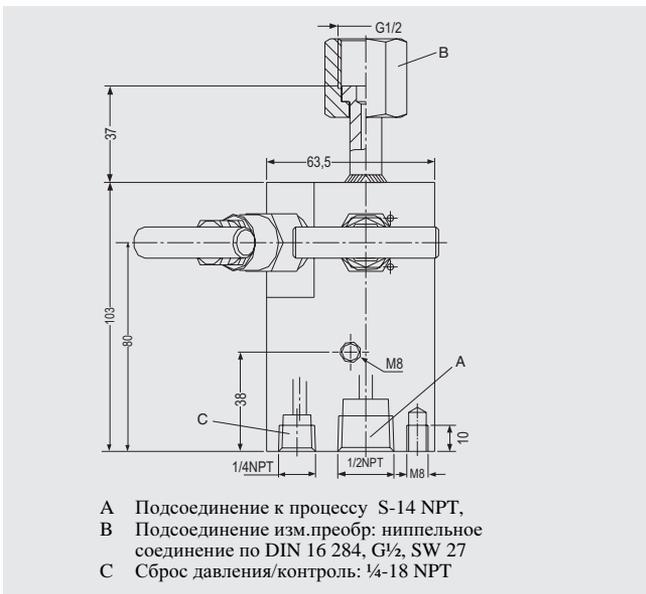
/107 2-х шпиндельный вентильный блок с вращающейся муфтой, размеры
